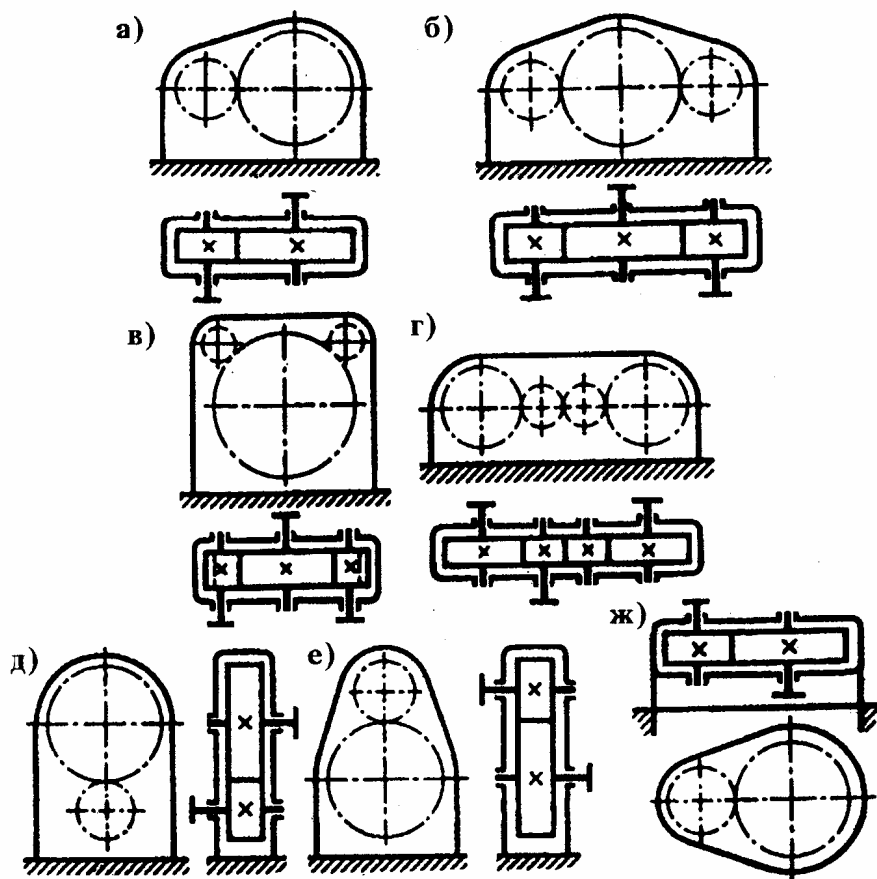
Кинематические схемы цилиндрических одноступенчатых редукторов (Ц)
